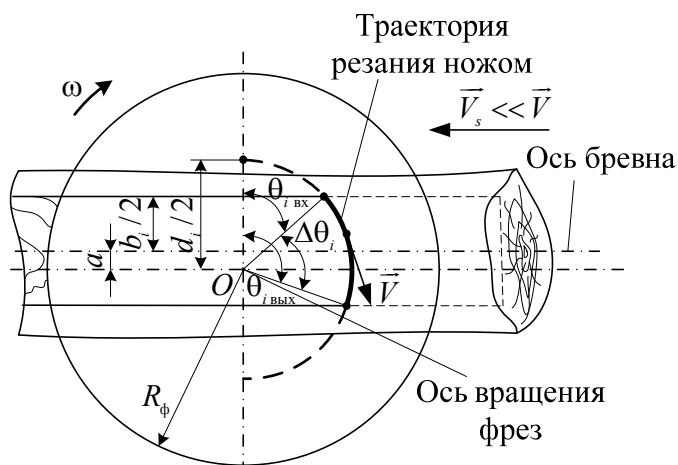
Общая схема обработки бревен на фрезерно-брусующем станке
